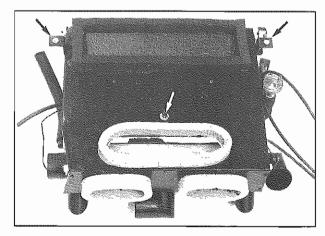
Viti fissaggio gruppo evaporatore Evaporator unit securing screws
